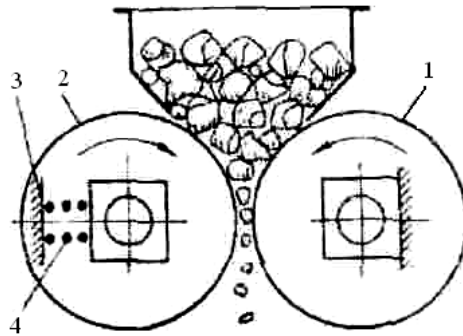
Схема роботи валкової дробарки: 1 – валок з нерухожими підшипниками; 2 – валок з рухомими підшипниками; 3 – корпус дробарки; 4 – пружини
